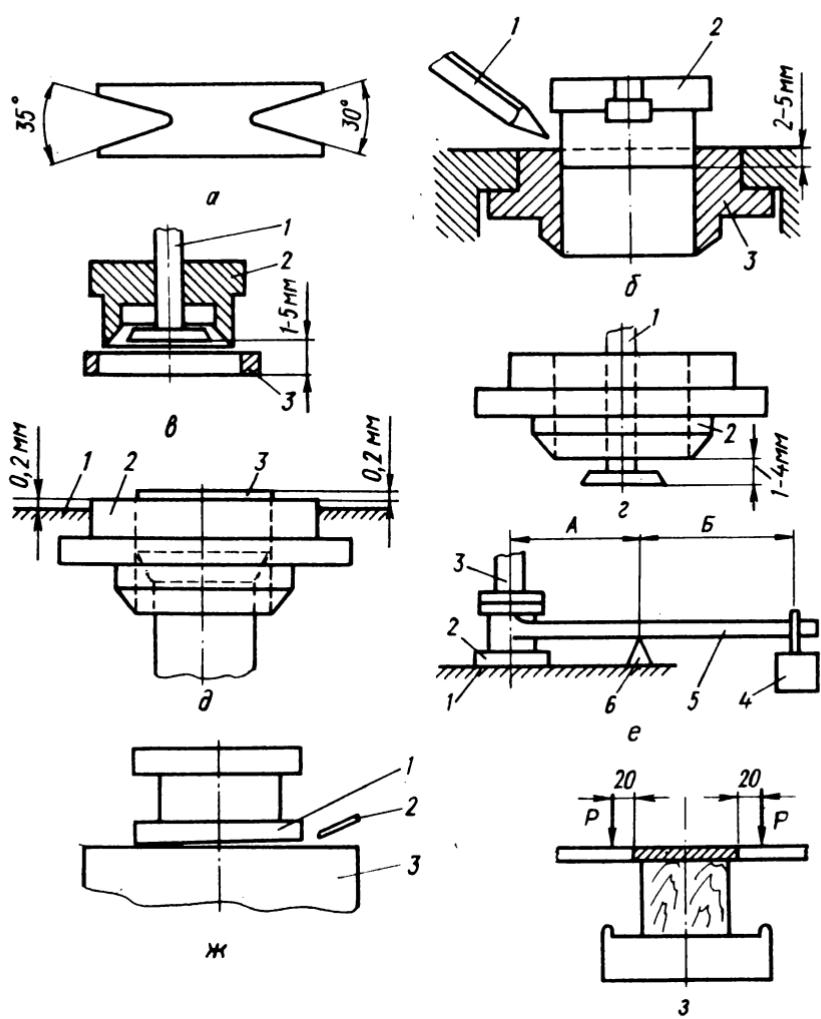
Схемы контроля состояния шпонопочиночного станка и качества починки шпона (а—з)
